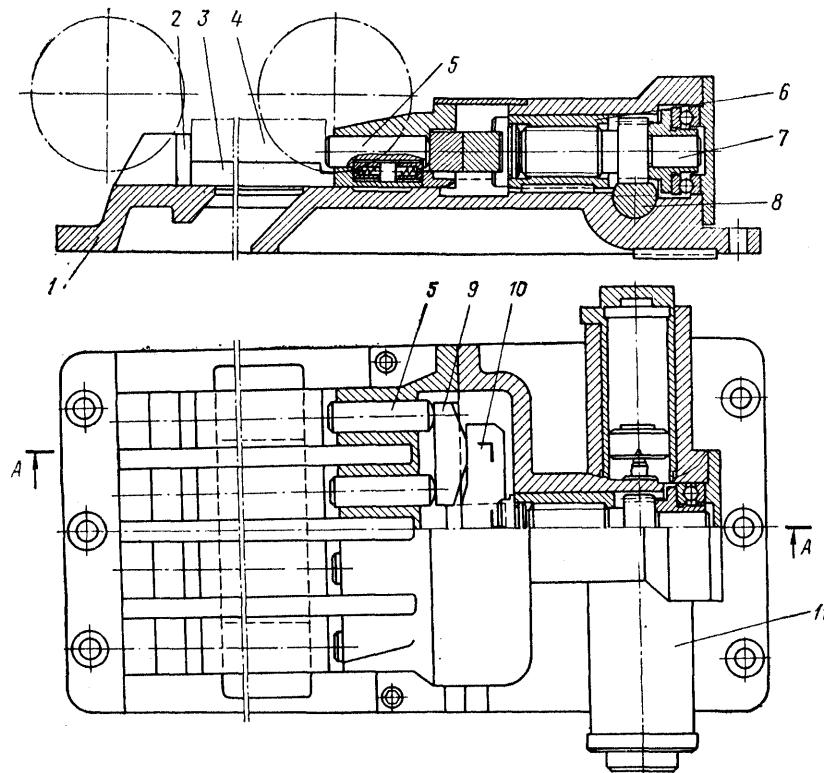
Приспособление для разрезки заготовок на полуавтомате модели 6В2
